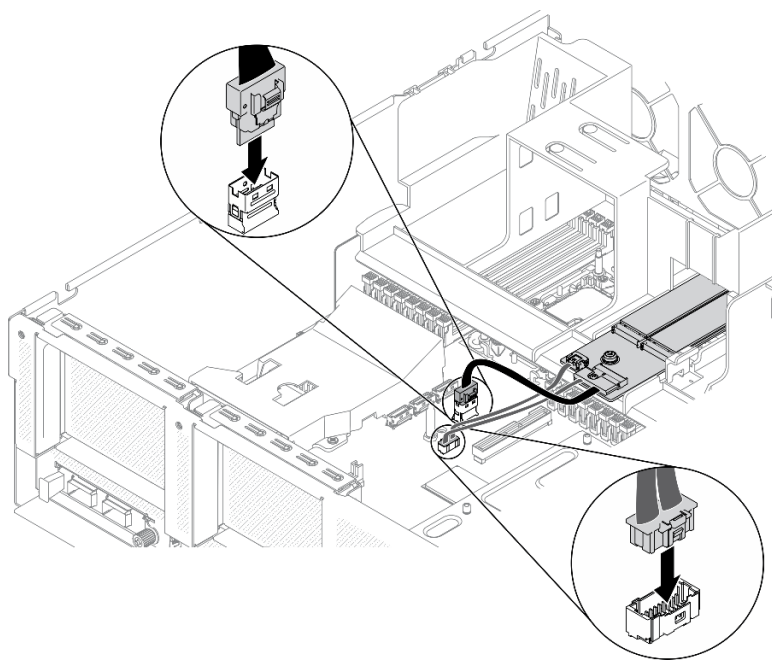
Conexión de los cables de la placa posterior de M.2 a la placa del sistema
